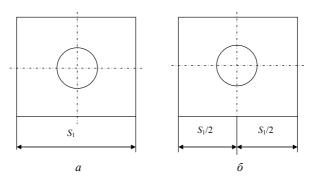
a – размеры на чертеже детали; δ – размеры на схеме обработки
